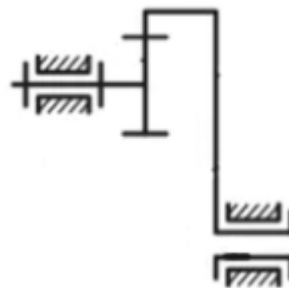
Кинематическая схема цилиндрического редуктора с внутренним зацеплением
